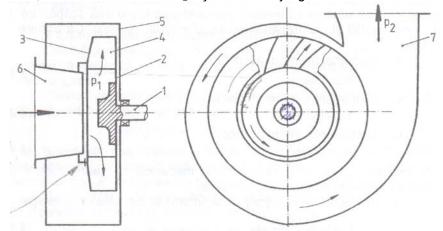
Ventilator centrifug: 1 - arbore; 2 - disc; 3 - capac; 4 - palete; 5 - carcasă; 6 - gură de aspirație; 7 - gură de refulare
